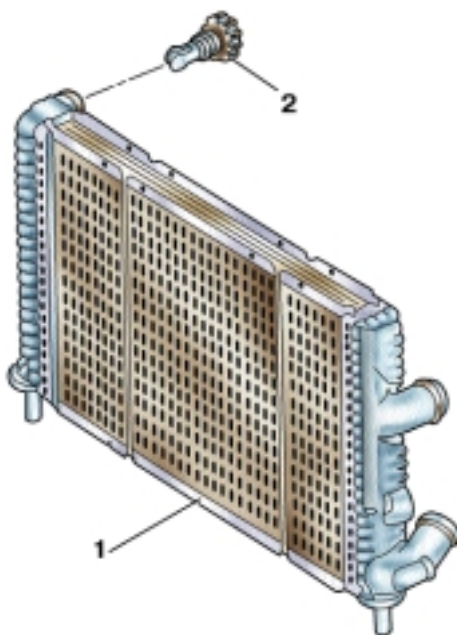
Расположение пробки отверстия для выпуска воздуха из системы охлаждения двигателя F3R 272: 1 – радиатор; 2 – пробка отверстия для выпуска воздуха
